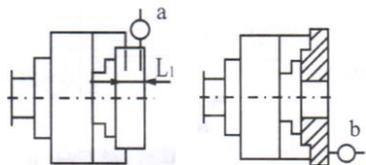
Токарный патрон с креплением заготовки за внешнюю поверхность с помощью обратных кулачков:
